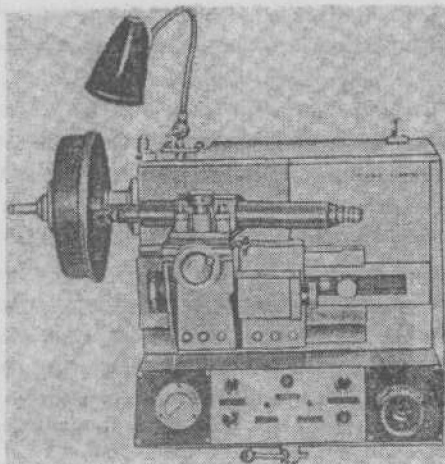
Станок для расточки тормозных барабанов и обточки тормозных накладок легковых автомобилей, мод. Р-117
